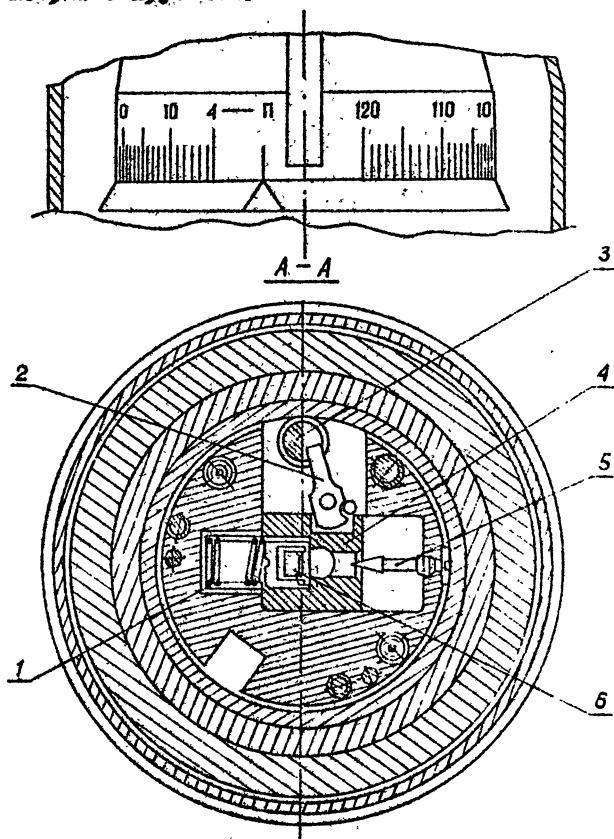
Шкала и детали ударно-спускового механизма взрывателя ИМ-120:
